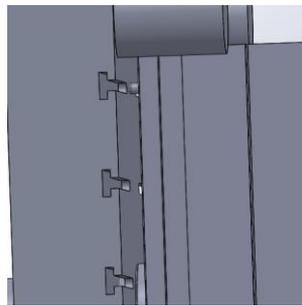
Encaixe do pino de centragem com o prato da máquina
